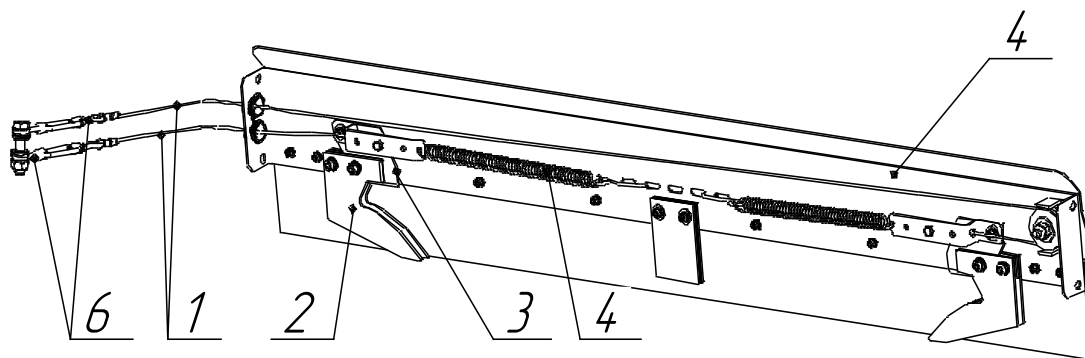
Режущий механизм: 1 – тросовый привод; 2 – нож; 3 – направляющие пластины; 4 – корпус; 5 – пружина; 6 - стяжка винтовая (талреп).
